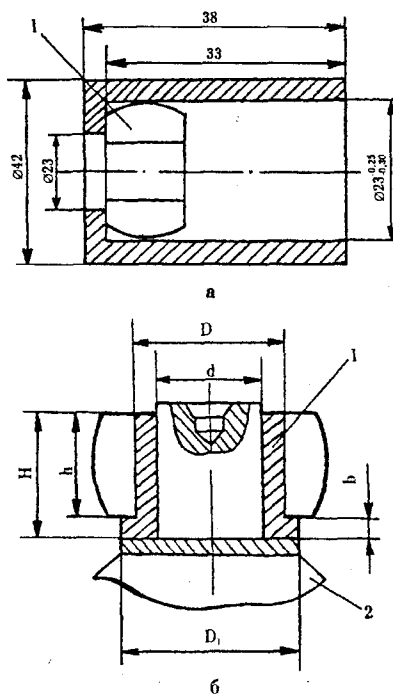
Детали для ремонта трехшиповика: а – оправка; 1 – сферический сухарь; б – отремонтированный трёхшиповик; 1 – бронзовая втулка; D – внешний диаметр втулки; d – внутренний диаметр втулки; D₁ – диаметр бурта втулки; b – толщина бурта; h – высота сферического сухаря; H – высота втулки; 2 – корпус трехшиповика
